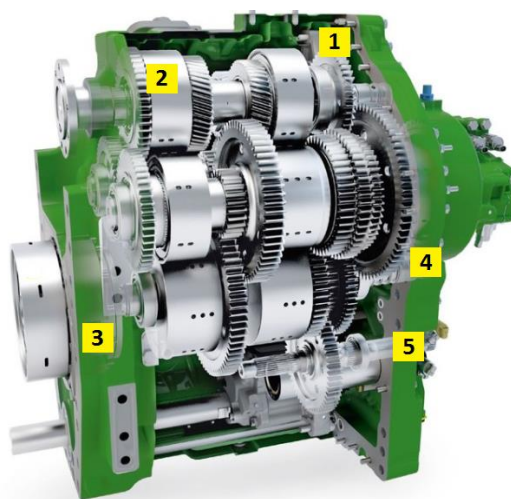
Převodovka Full Power Shift 18/4 [2]
